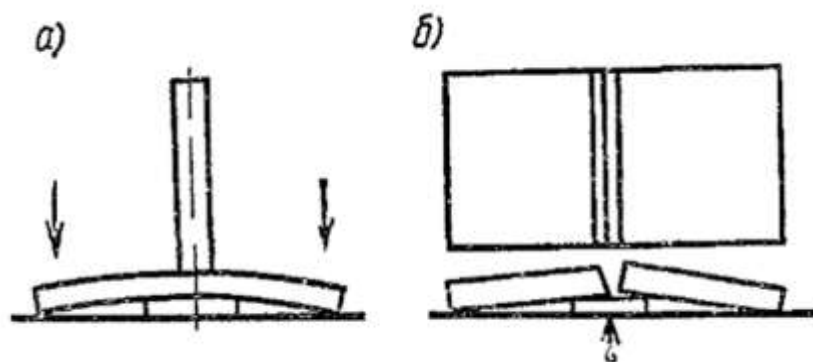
Предварительный обратный выгиб для предупреждения угловой деформации: а — полки балок, б — листов резервуара.
